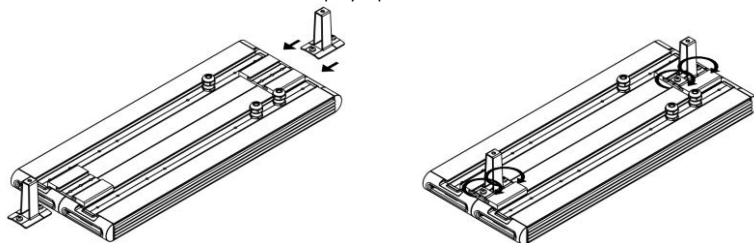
Установка крепления на соединительные планки на примере светильника Element 0,5x2 и Крепления Подвес.
